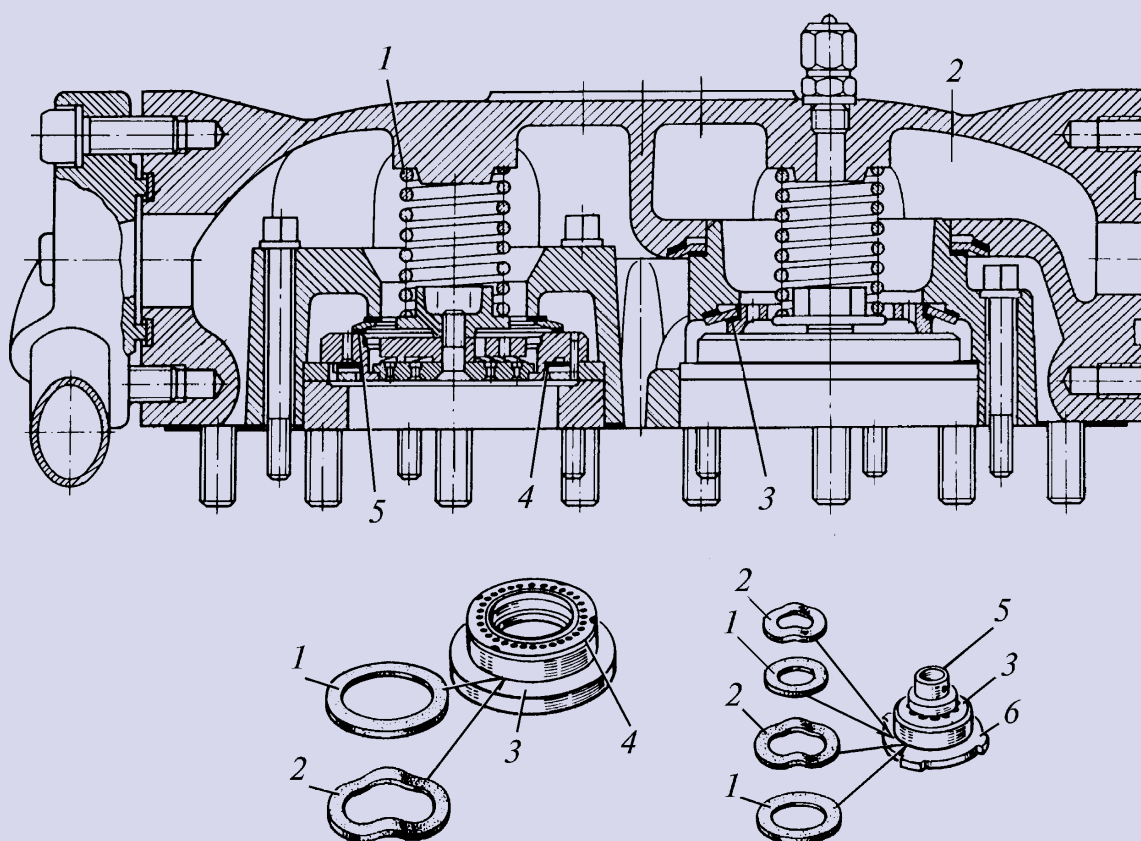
Головка цилиндров: 1 — нажимная пружина; 2 — камера; 3 — кольцо; 4 — всасывающий клапан; 5 — прижимная поверхность
